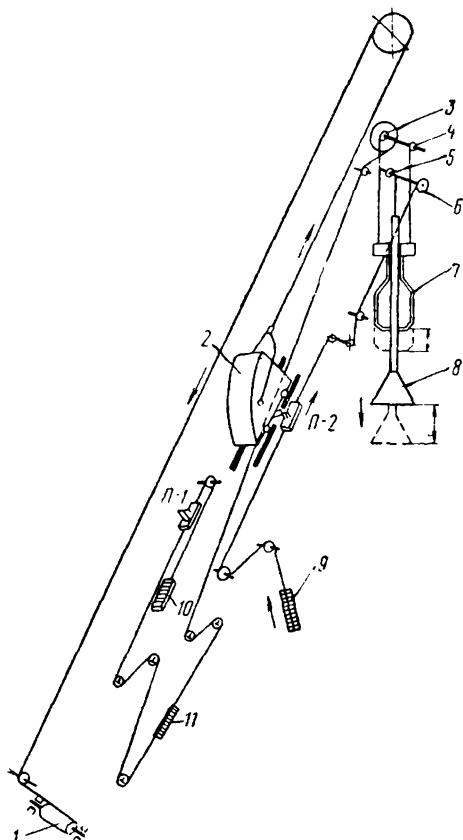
Кинематическая схема автоматической работы загрузочного устройства шахтной печи:
